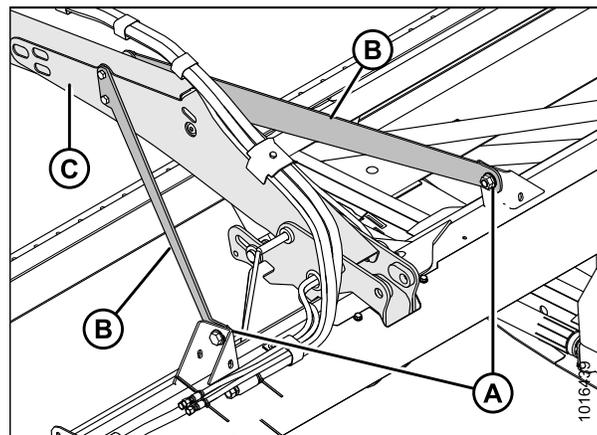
Центральный опорный рычаг подбирающего мотовила
